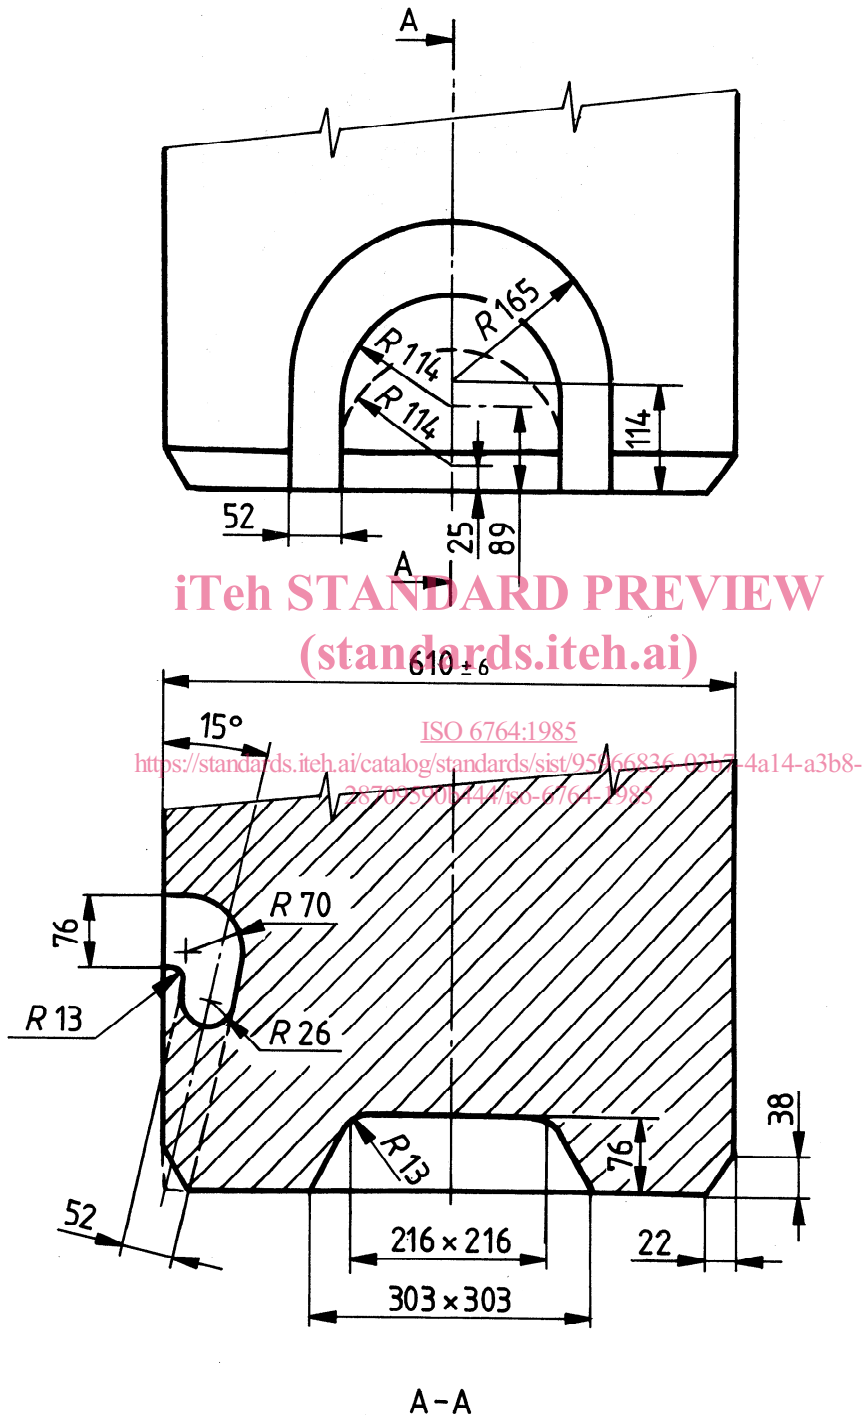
Dimensions de la pièce coulée inférieure d'un montant de levage
